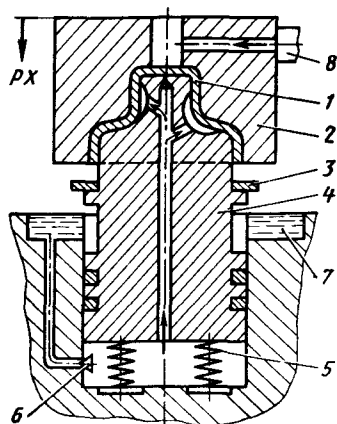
Схема гидроформирования конуса жаровой трубы:
